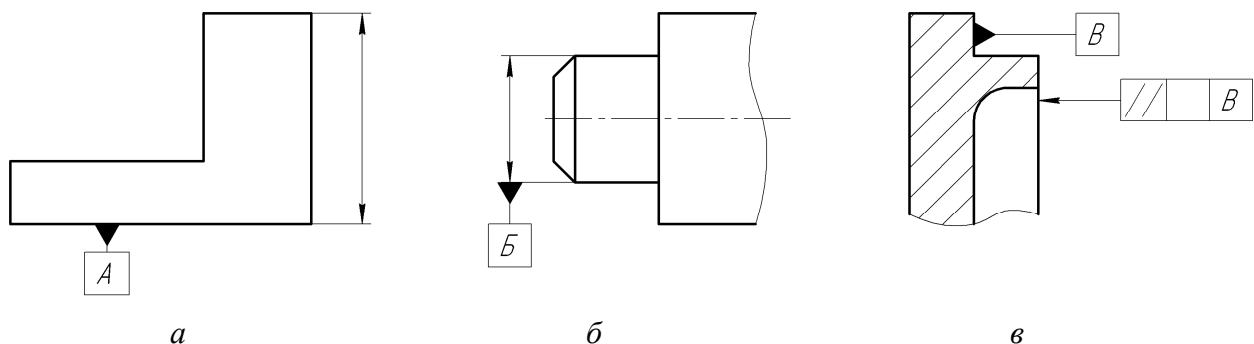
Правила нанесения условных обозначений баз на чертежах деталей
